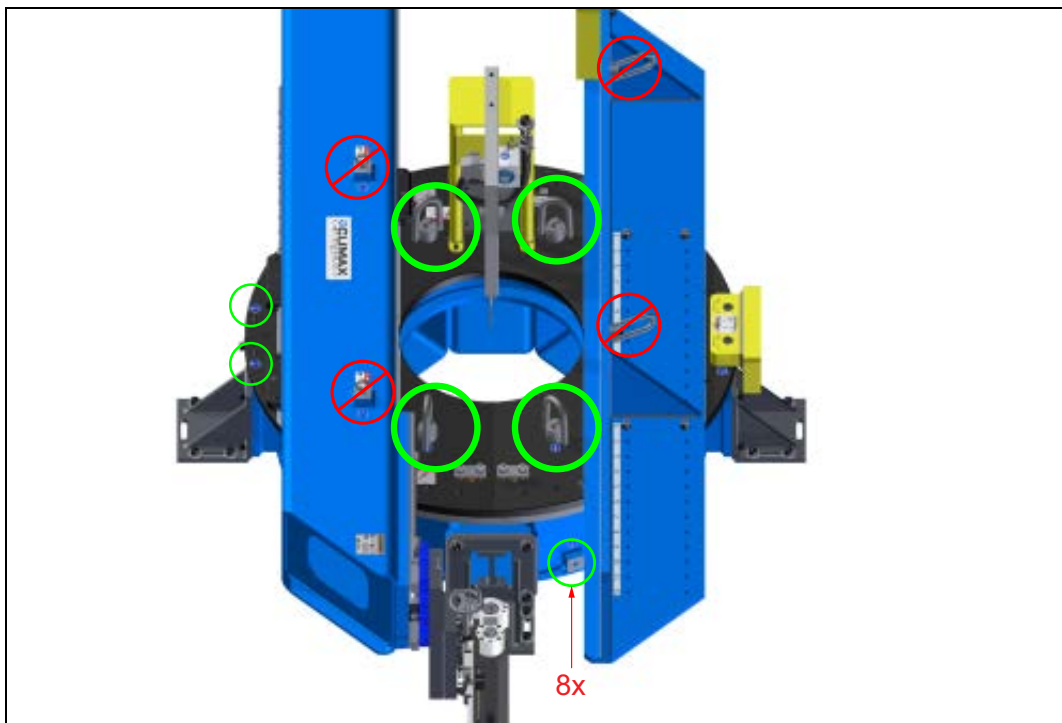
ANNEAUX DE LEVAGE POUR LE LEVAGE DE LA MACHINE ASSEMBLÉE
